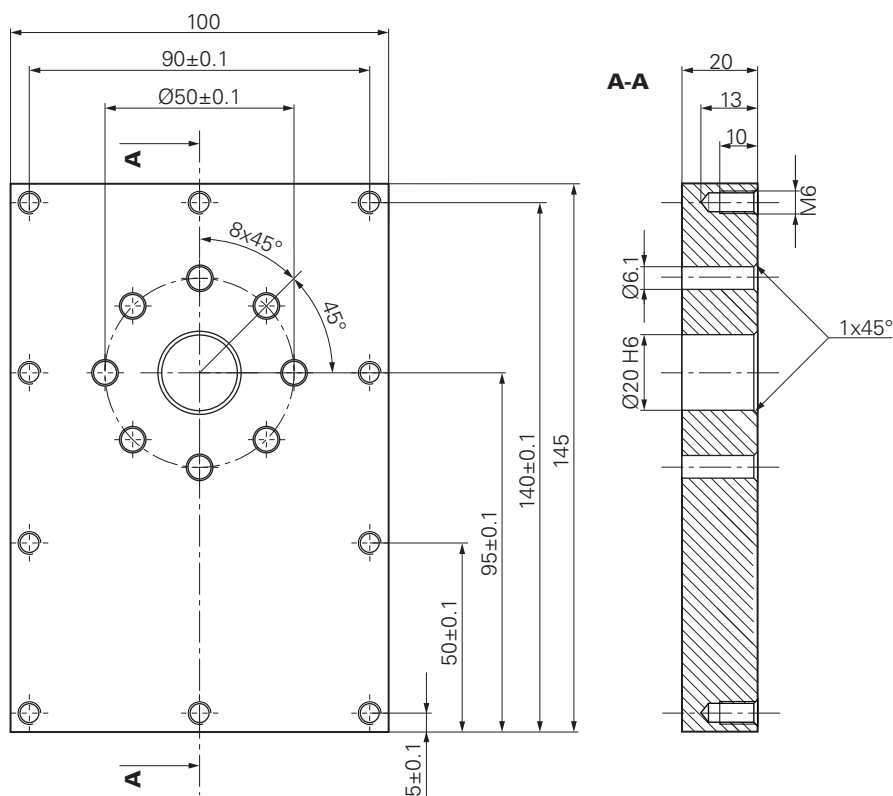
Peça de trabalho de exemplo – Desenho Técnico
